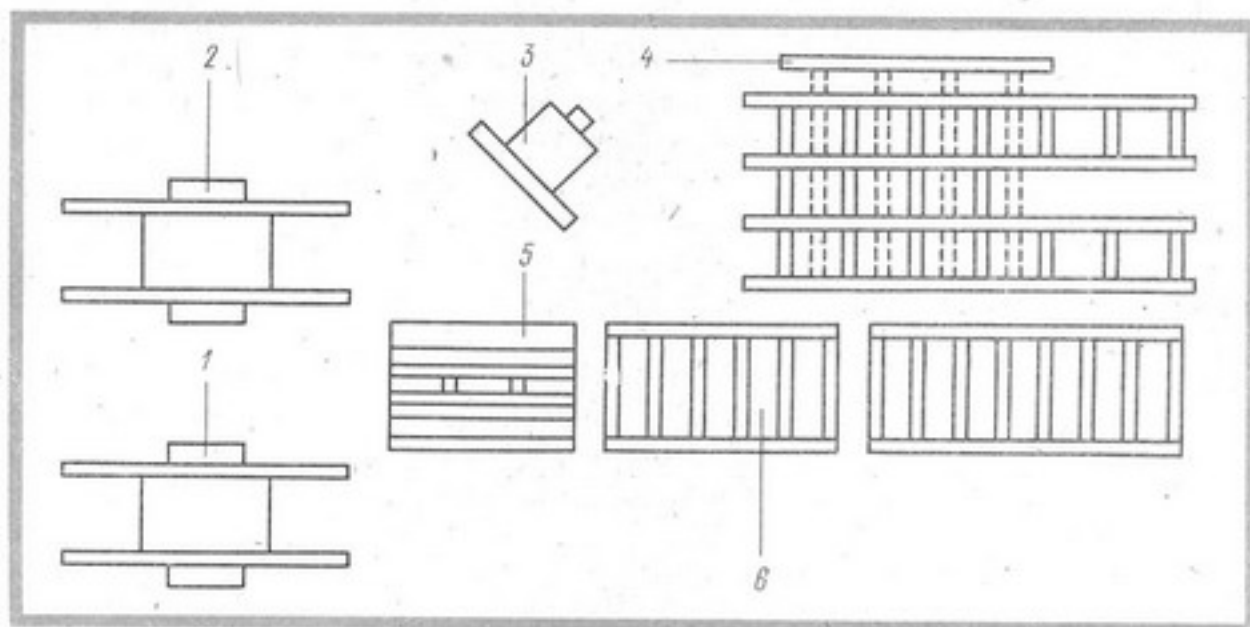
Схема линии ОК509 по резке шипов в брусках и сборке створок:
